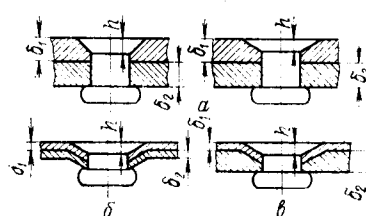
Способы выполнения гнезд под потайные головки заклепок: а — зенкованием; б — штамповкой; в — штамповкой в одной детали, зенкованием в другой детали.
